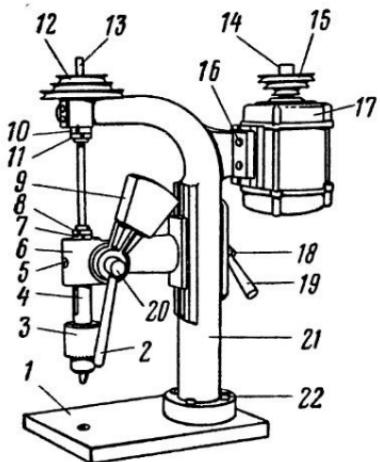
Настольно-сверлильный станок: 1 — основание; 2 — ручка; 3 — сверлильный патрон; 4 — пиноль; 5 — стопорный винт; 6 — траверза; 7 — гайка; 8 — контргайка; 9 — противовес; 10 — гайка; 11 — контргайка; 12 — ведомый шкив; 13 — шпиндель; 14 — вал электродвигателя; 15 — ведущий шкив; 16 — болт; 17 — электродвигатель; 18 — затяжной болт; 19 — зажимная ручка; 20 — зубчатый валик (валик-шестерня); 21 — колонка; 22 — болт.
